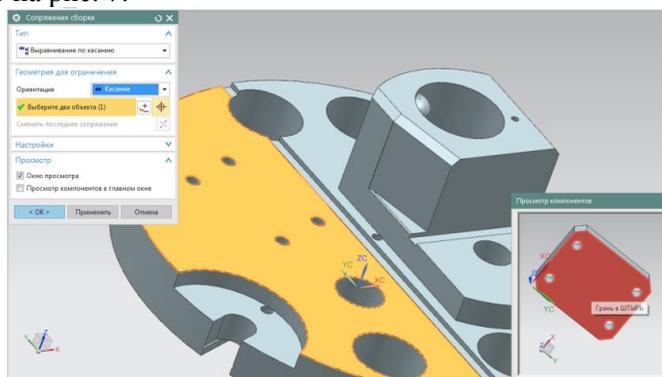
Сопрежение нижней поверхности детали «опора» с верхней поверхностью детали «плита»
